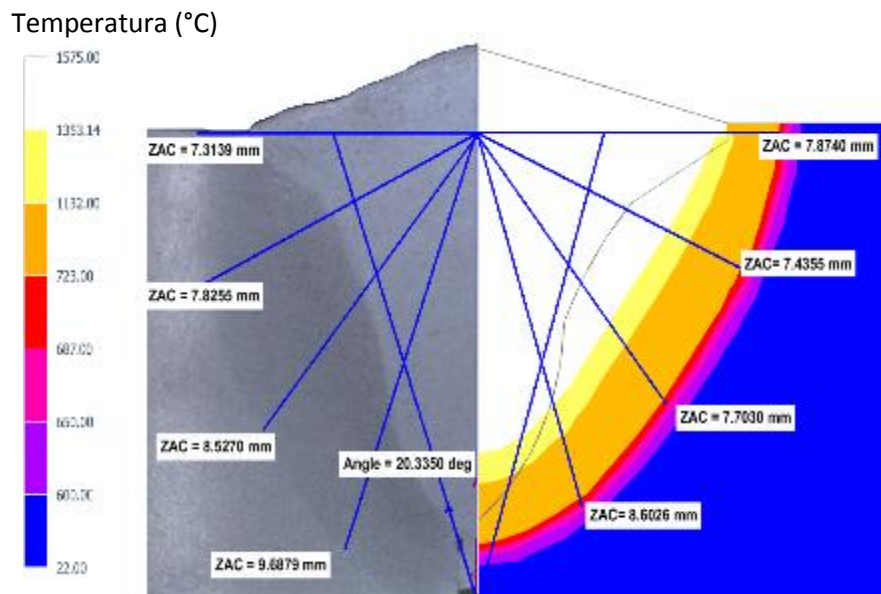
Isotermas de la sección transversal del cordón de soldadura con geometría real modelada. A la izquierda se presenta la experimentación y a la derecha la solución numérica.
